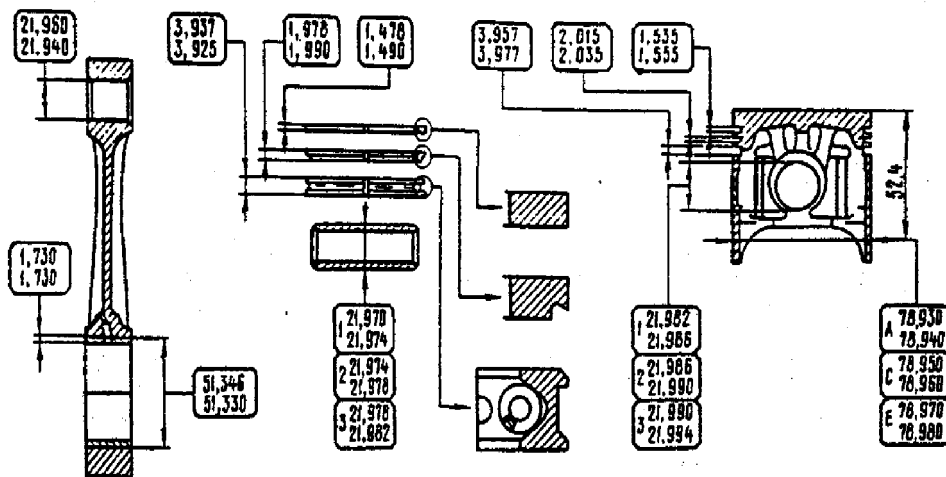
Dimensões dos êmbolos, bielas, pinos e anéis de segmento
